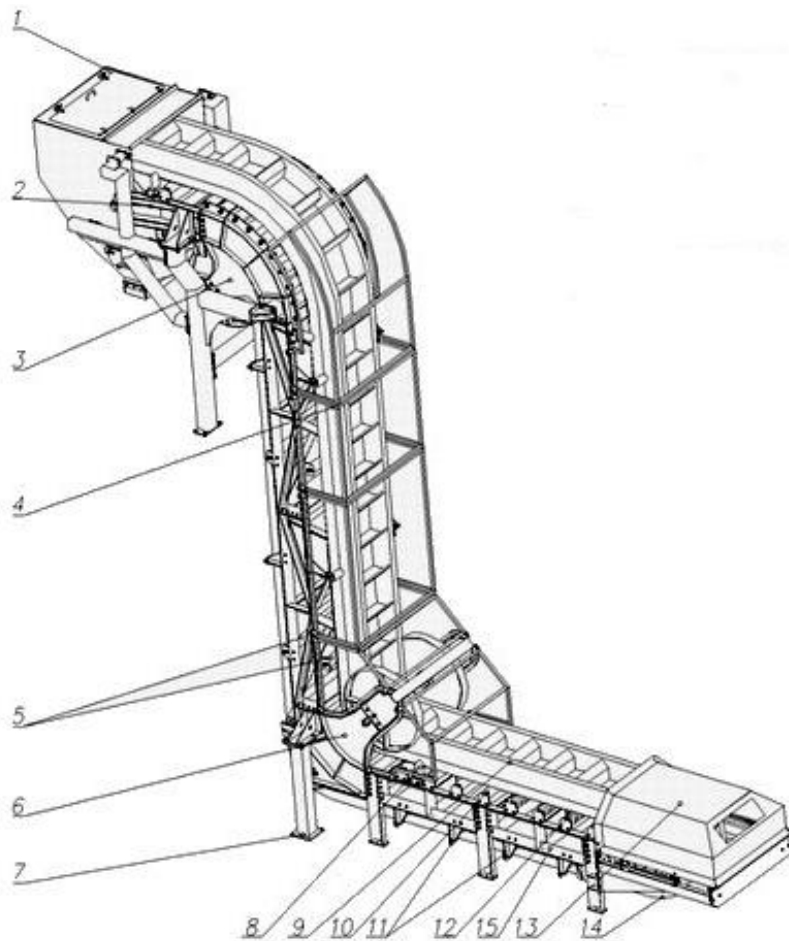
Конструктивная схема Z-образного конвейера:
